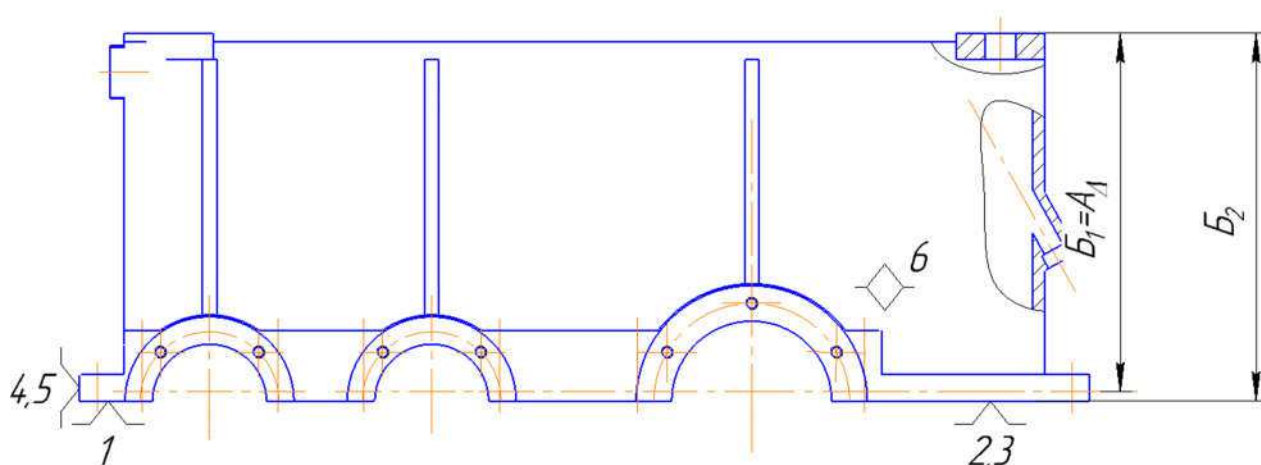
Схема базирования корпуса по плоскости разъема и стенкам корпуса.
